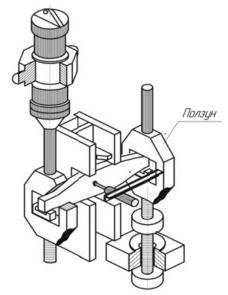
Общий вид механизма подъема ПБУ «Каспий»
